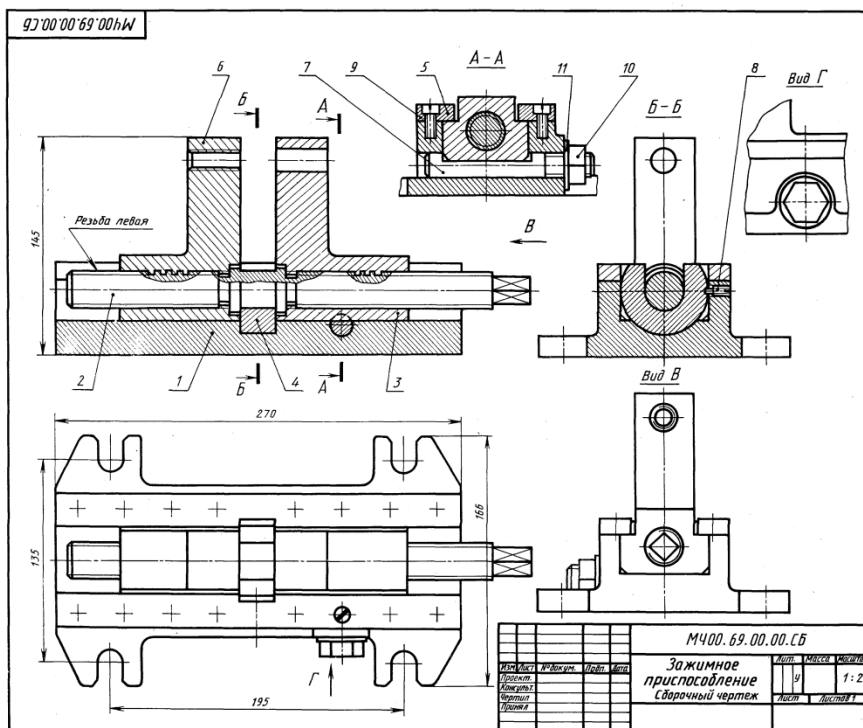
Сборочный чертеж «Зажимное приспособление»
